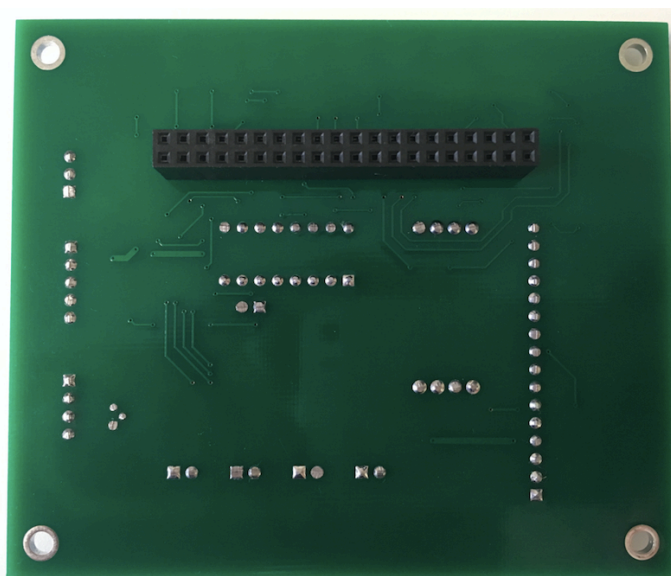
Imagen de capa *bottom* de la PCB real una vez se han soldado los diferentes componentes sobre la placa.
